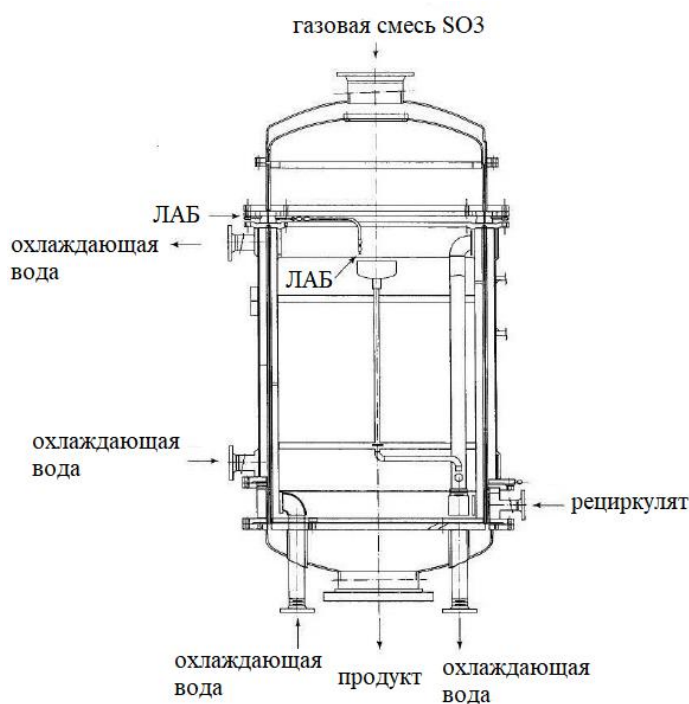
Цилиндрический пленочный реактор [19, 20]
